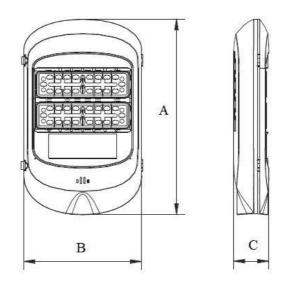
Вид светильника ДКУ61 (корпус Winner 2)
